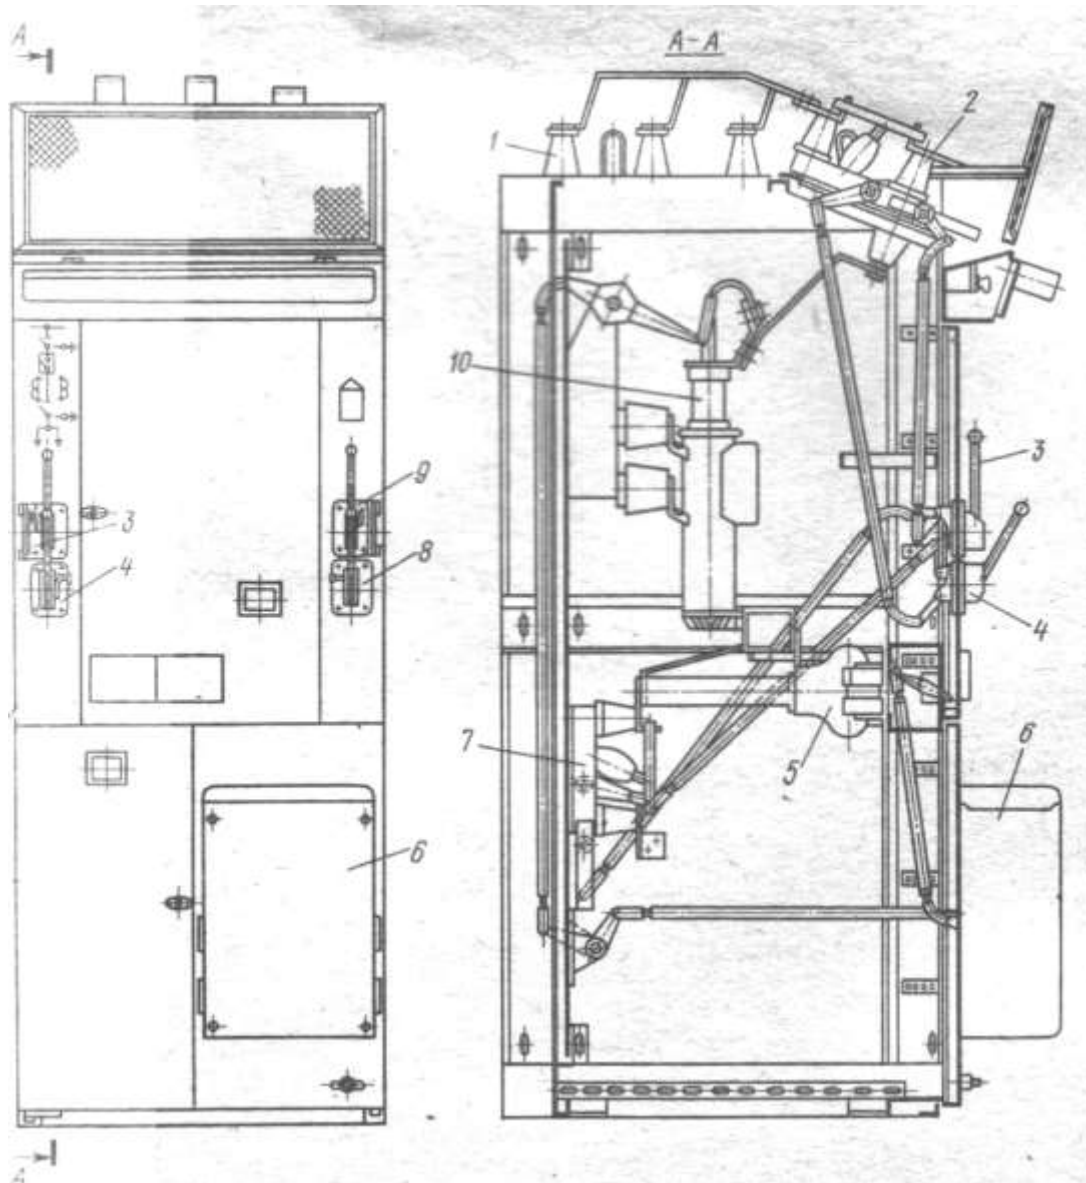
Камера серии КСО-272 с выключателем ВМГ-10: 1— сборные шины, 2—шинный разъединитель, 3—привод заземляющих ножей шинного разъединителя. 4—привод шинного разъединителя, 5—трансформатор тока, 6—пружинный привод ПП-67, 7—линейный разъединитель, 8—привод линейного разъединителя, 9—привод заземляющих ножей линейного разъединителя, 10—выключатель ВМГ-10.
